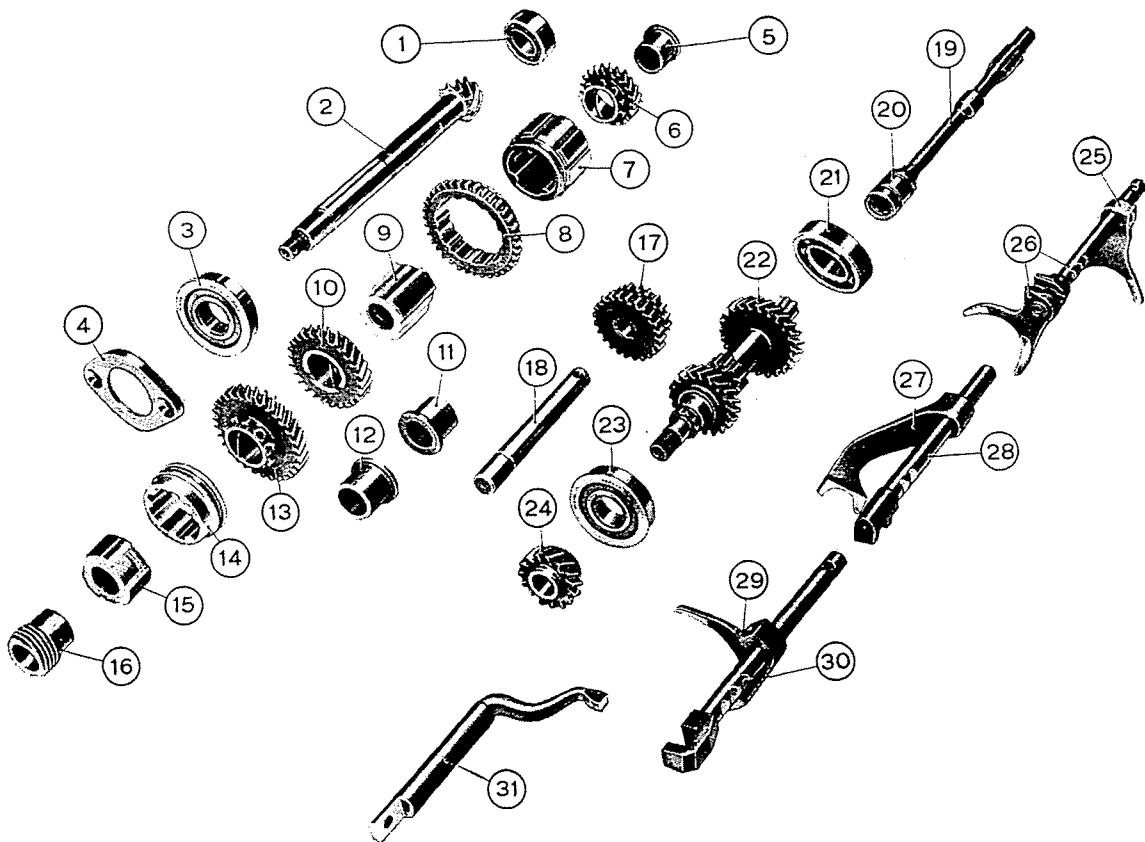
Einzelteile des Wechselgetriebes zur Gangumschaltung.
